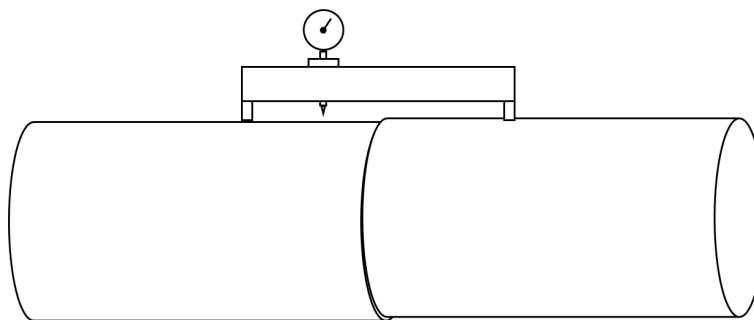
Medición con regla comparadora. Soldadura circunferencial desalineada.
